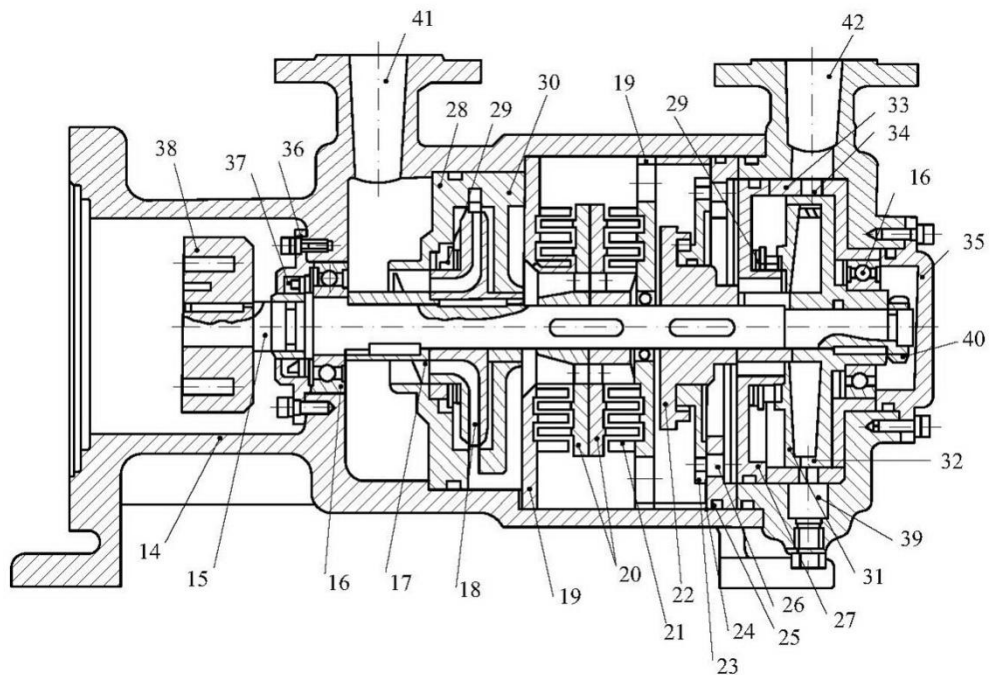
Конструктивная схема диспергирующего устройства в виде четырехступенчатой гидродинамической системы: 14 – корпус; 15 – вал; 16 – опорные подшипники; 17 – шнек; 18 – насосное колесо; 19 – зубчатый ротор и статор; 20 – статор с прорезями 21; 22 – ступица; 23 – дисковый ротор с отверстиями 24; 25 – дисковый статор с отверстиями 26; 27, 28 – диафрагмы; 29 – уплотнения; 30 – направляющий аппарат; 31 – радиальный ротор с отверстиями 34; 35, 36 – крышки; 37 – манжетные уплотнения; 38 – полумуфта; 39 – камера озвучивания; 40 – защитные пластины для подшипников; 41, 42 – входной и выходной патрубки
